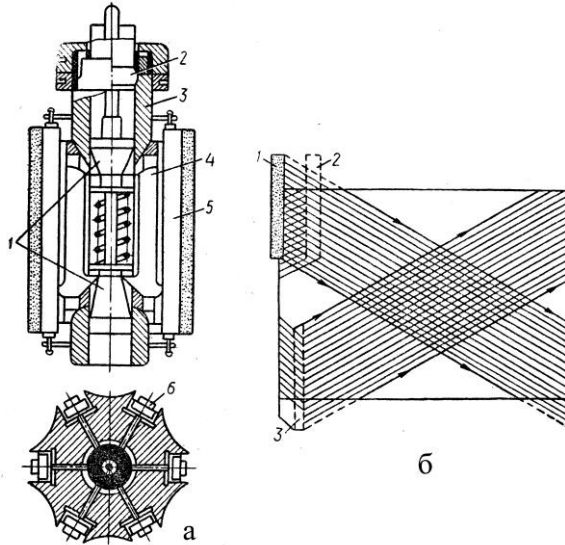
Хонінгування гільз циліндрів: а – схема хонінгувальної головки: 1 – розсувні конуси; 2 – шарнір; 3 – корпус; 4 – упорна пластина; 5 – тримач бруска; б – сліди обробки після хонінгування за один подвійний хід головки на розгорнутій поверхні циліндра
